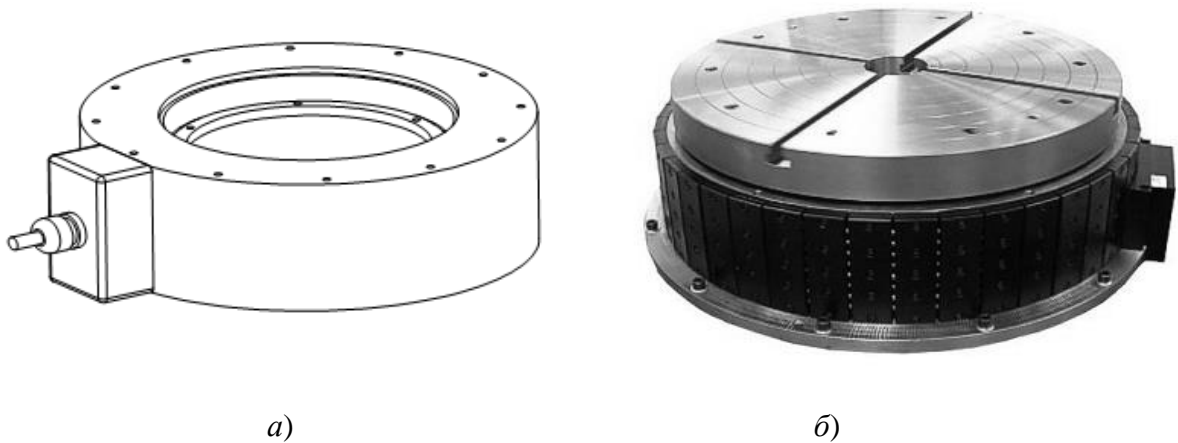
Поворотный стол: *а* – эскиз статора двигателя; *б* – общий вид поворотного стола фирмы Рухсервомотор
